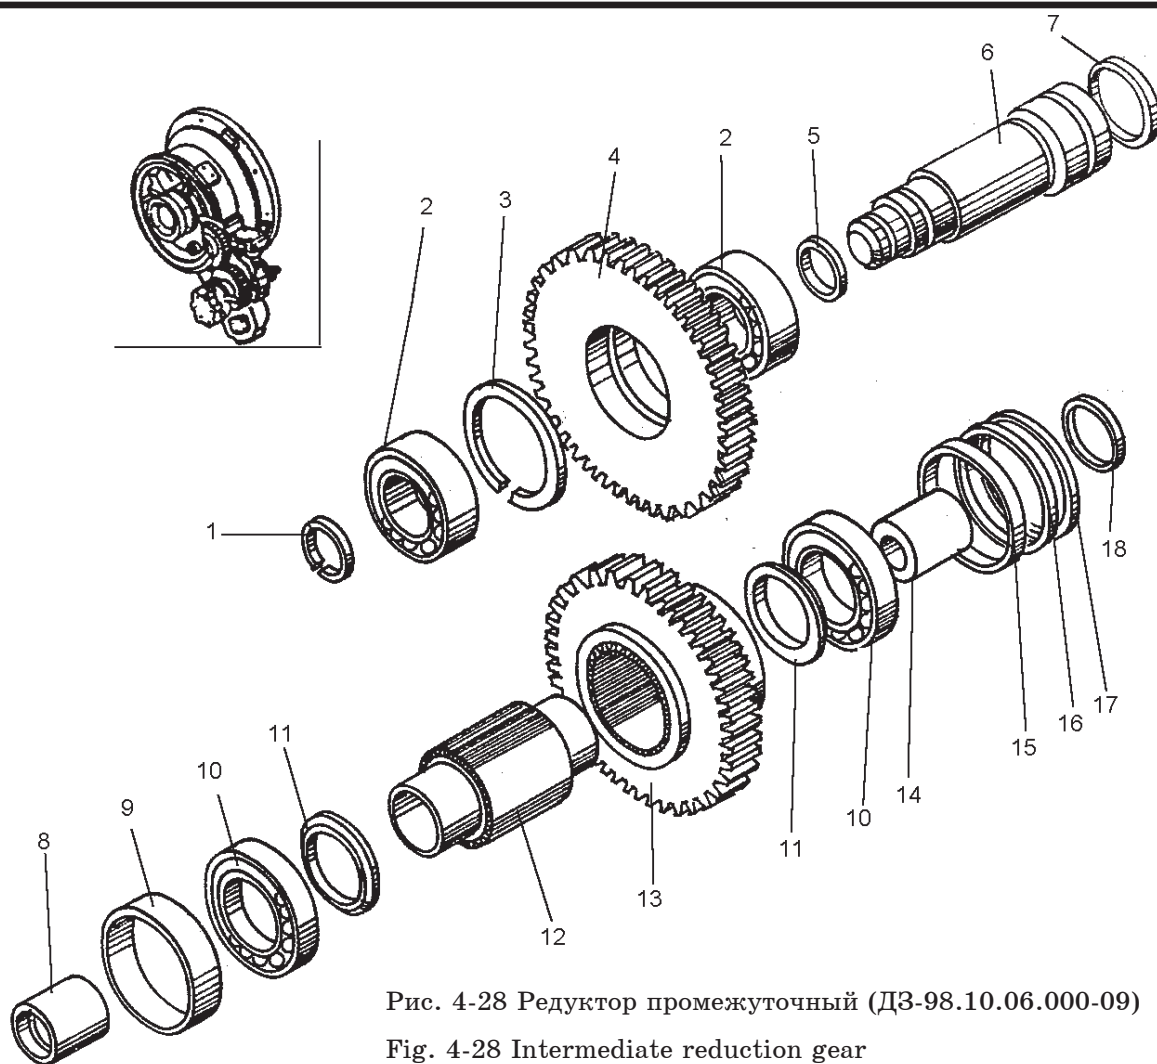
Редуктор промежуточный (ДЗ-98.10.06.000-09)
